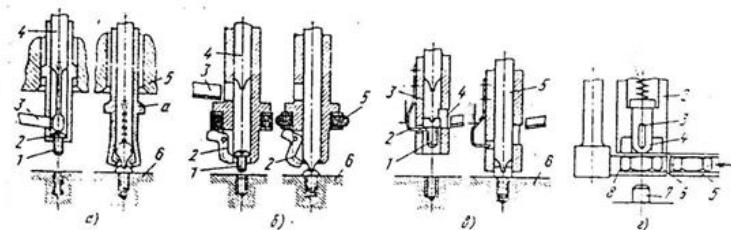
Конструкции питателей для подачи и завертывания резьбовых крепежных деталей
